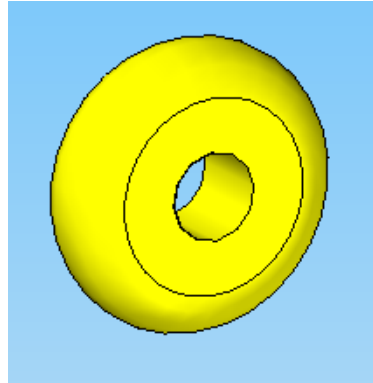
Rueda Hyper Hockey Pro 250 diseñada en Solid Edge
